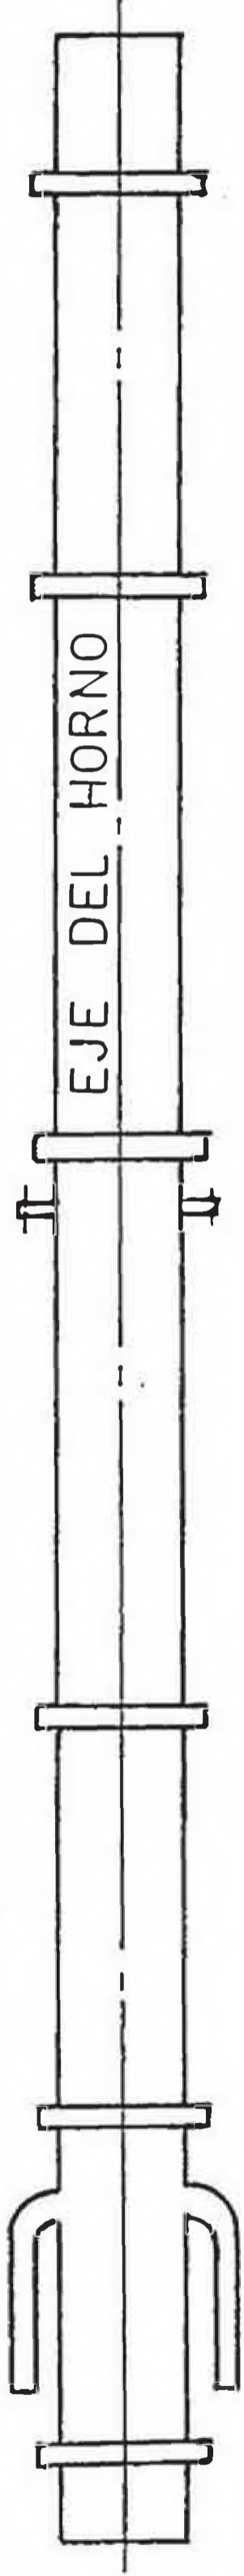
A VISTA DEL HORNO EN EL PLANO HORIZONTAL
